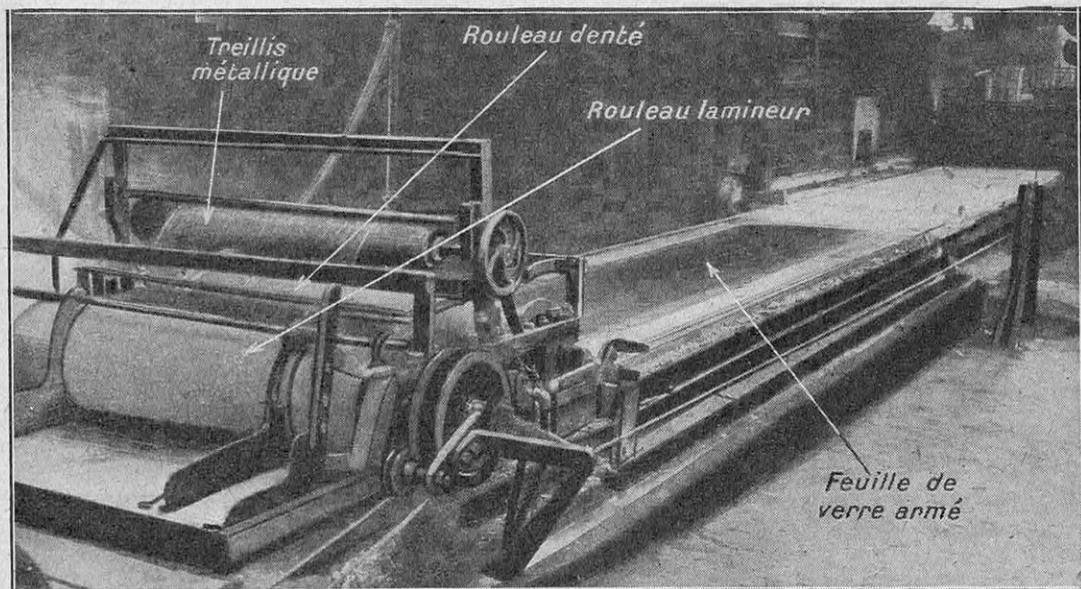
MACHINE « SCHUMANN » POUR LA FABRICATION DU VERRE ARMÉ
